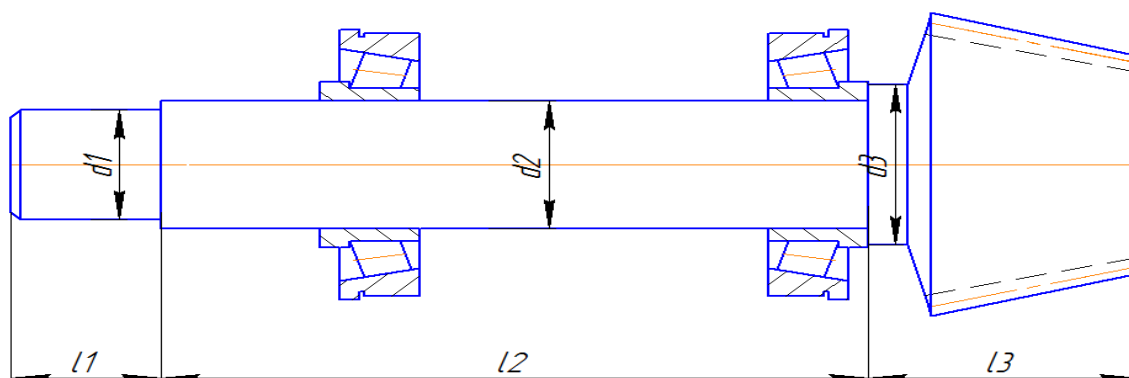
Проектный расчет быстроходного вала конического редуктора
